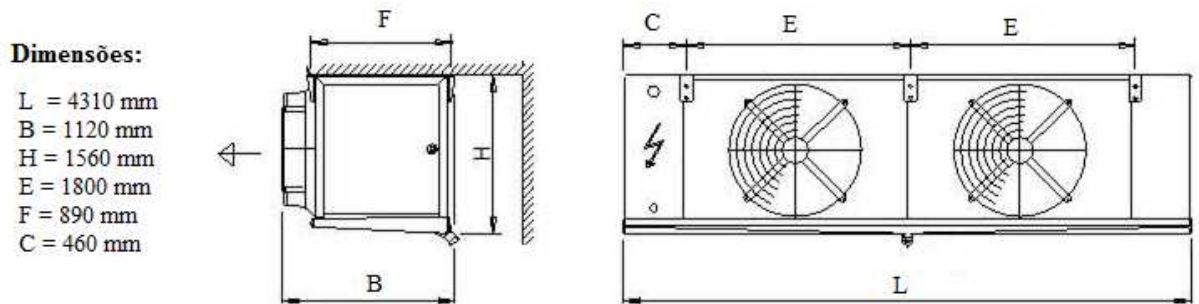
Dimensões do evaporador utilizado nos testes.
